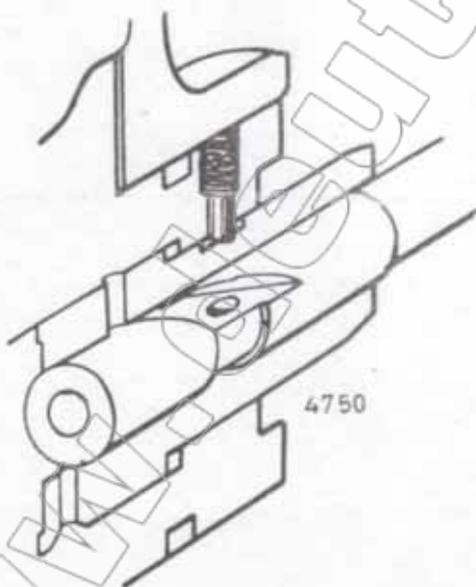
Fixierung des Pumpenzylinders im Pumpenblock
